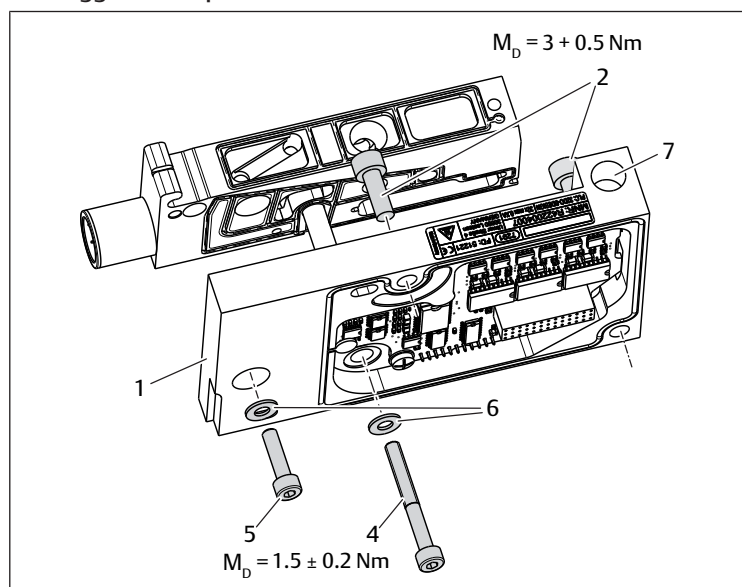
Montare il modulo adattatore AV05-B-Design su una piastra di adattamento AV03-AV05
